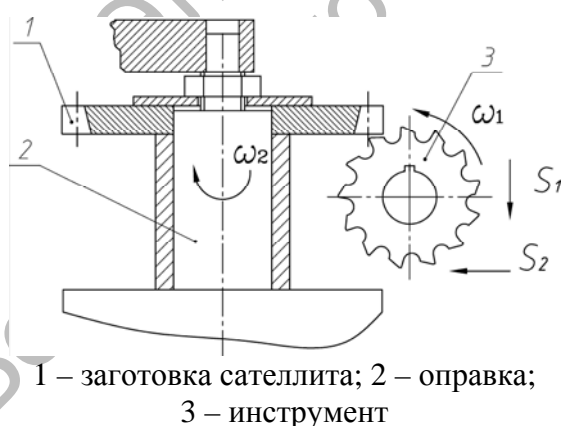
Схема установки фрезы относительно заготовки сателлита для нарезания зубьев способом двойного рабочего хода
